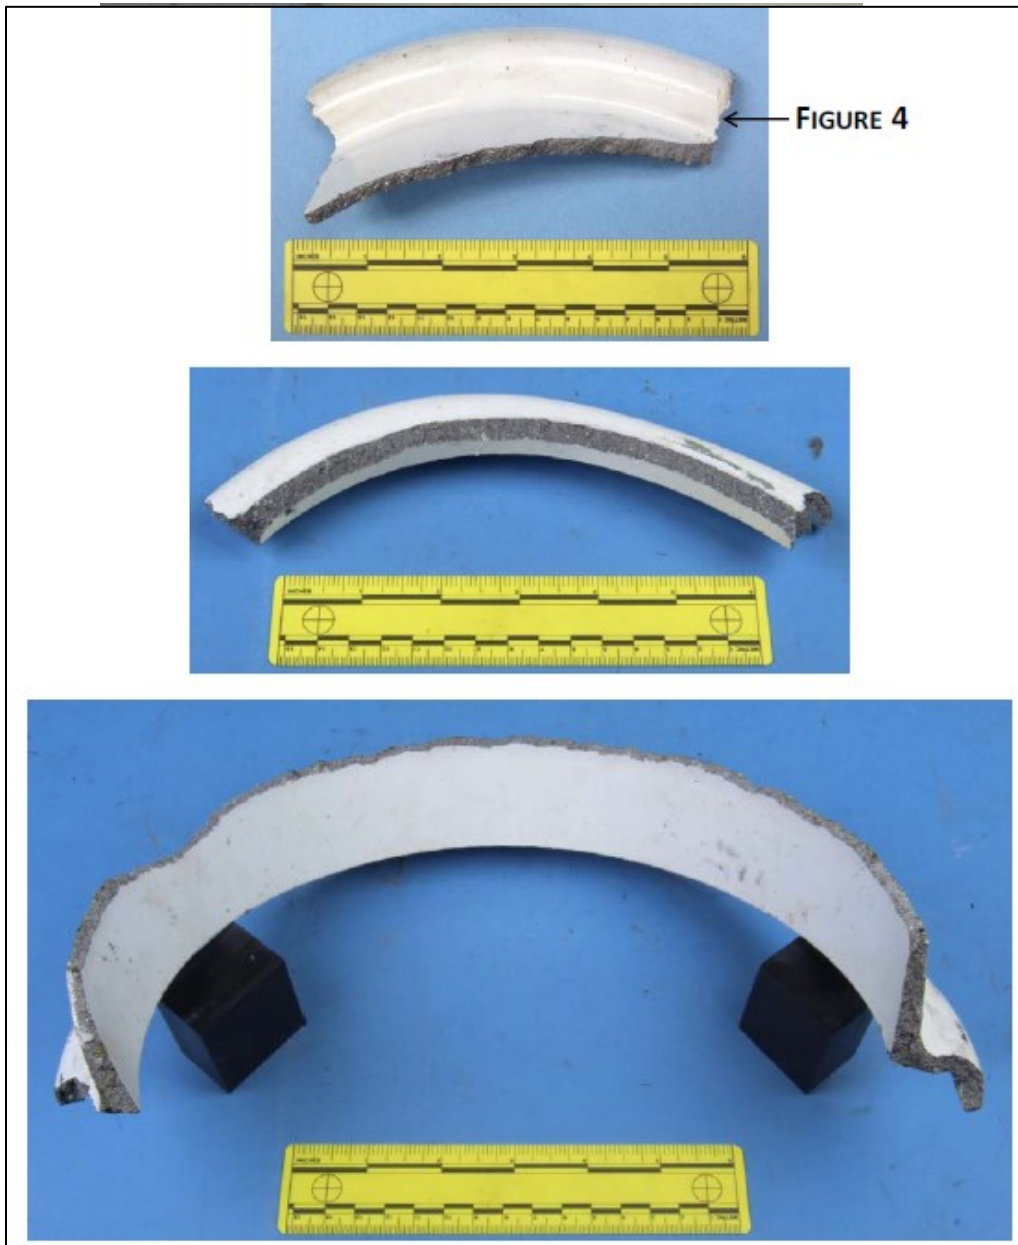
Fotos en primer plano de las superficies fracturadas, en las piezas de la llanta separadas del tren de aterrizaje.
